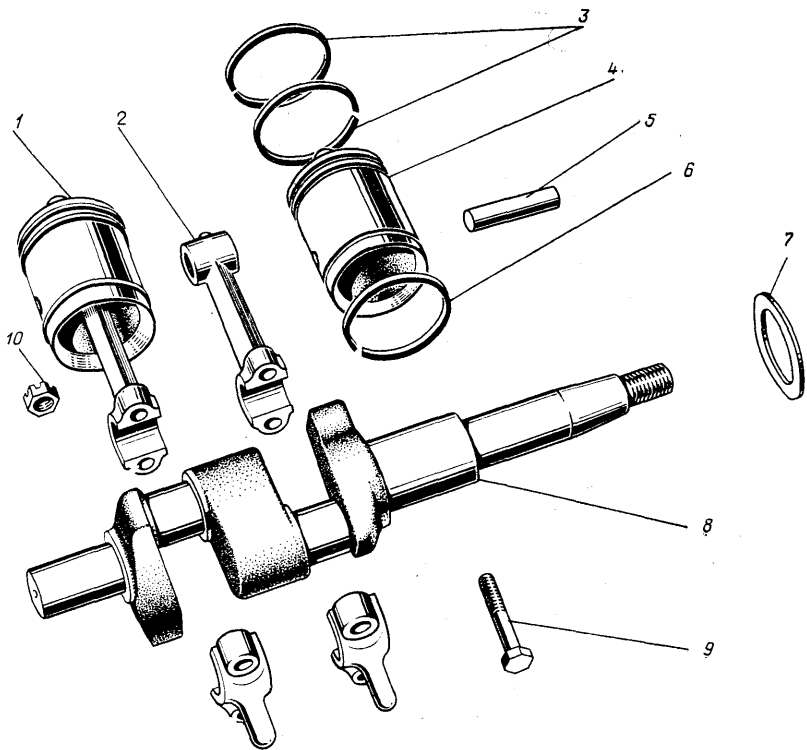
Детали механизма движения компрессора с коленчатым валом:
